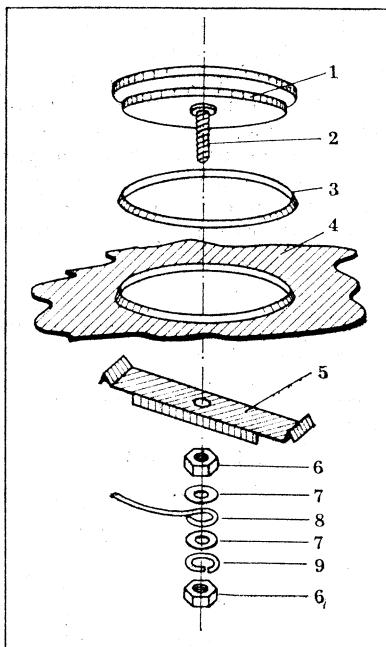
Элементы крепления чугунной конфорки на рабочем столе электроплиты: 1 — конфорка; 2 — шпилька М6×40; 3 — кольцо манжеты; 4 — рабочий стол; 5 — скоба; 6 — гайка; 7 — шайба; 8 — заземляющий провод; 9 — пружинная шайба
